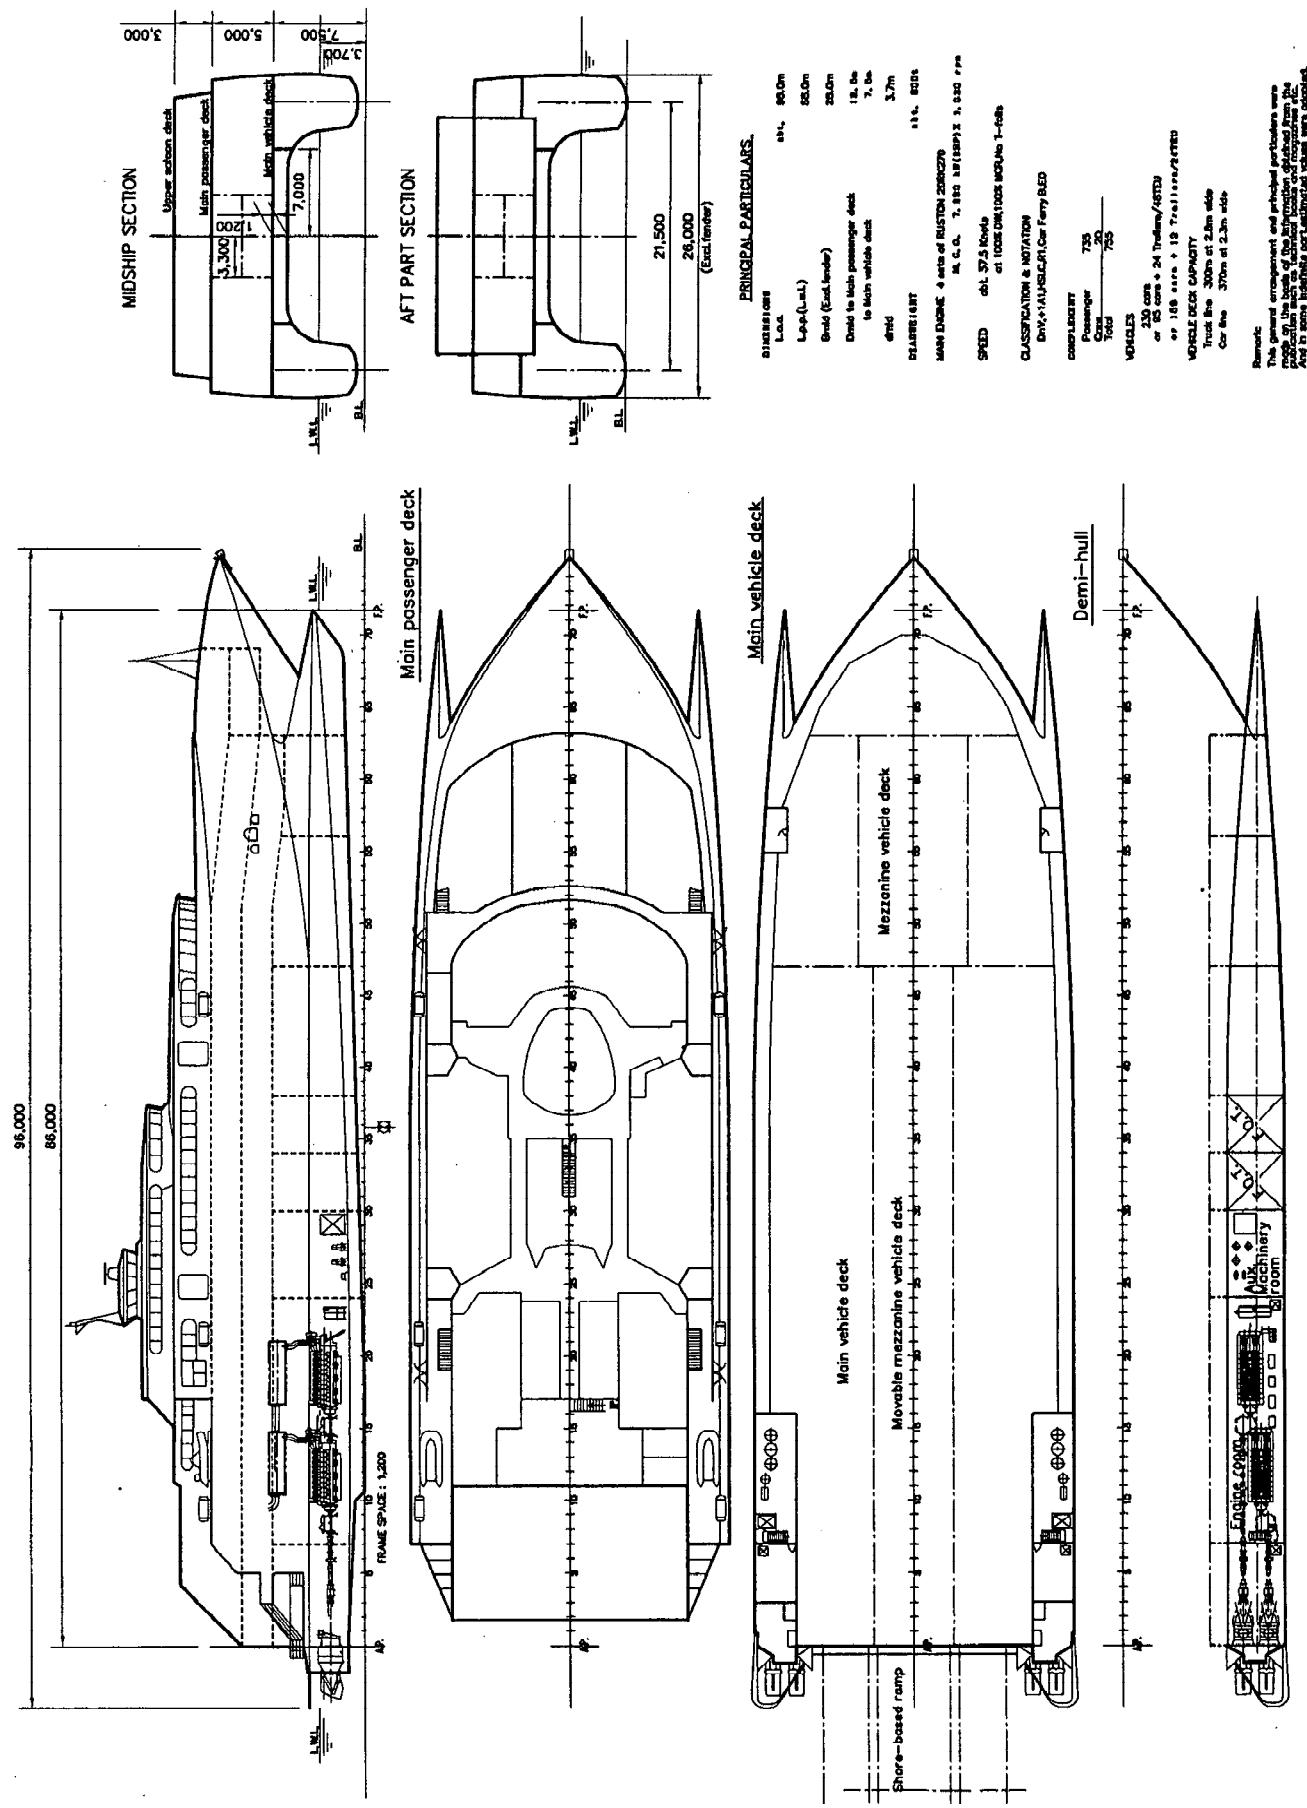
双胴船 INCAT 96m型一般配置図
